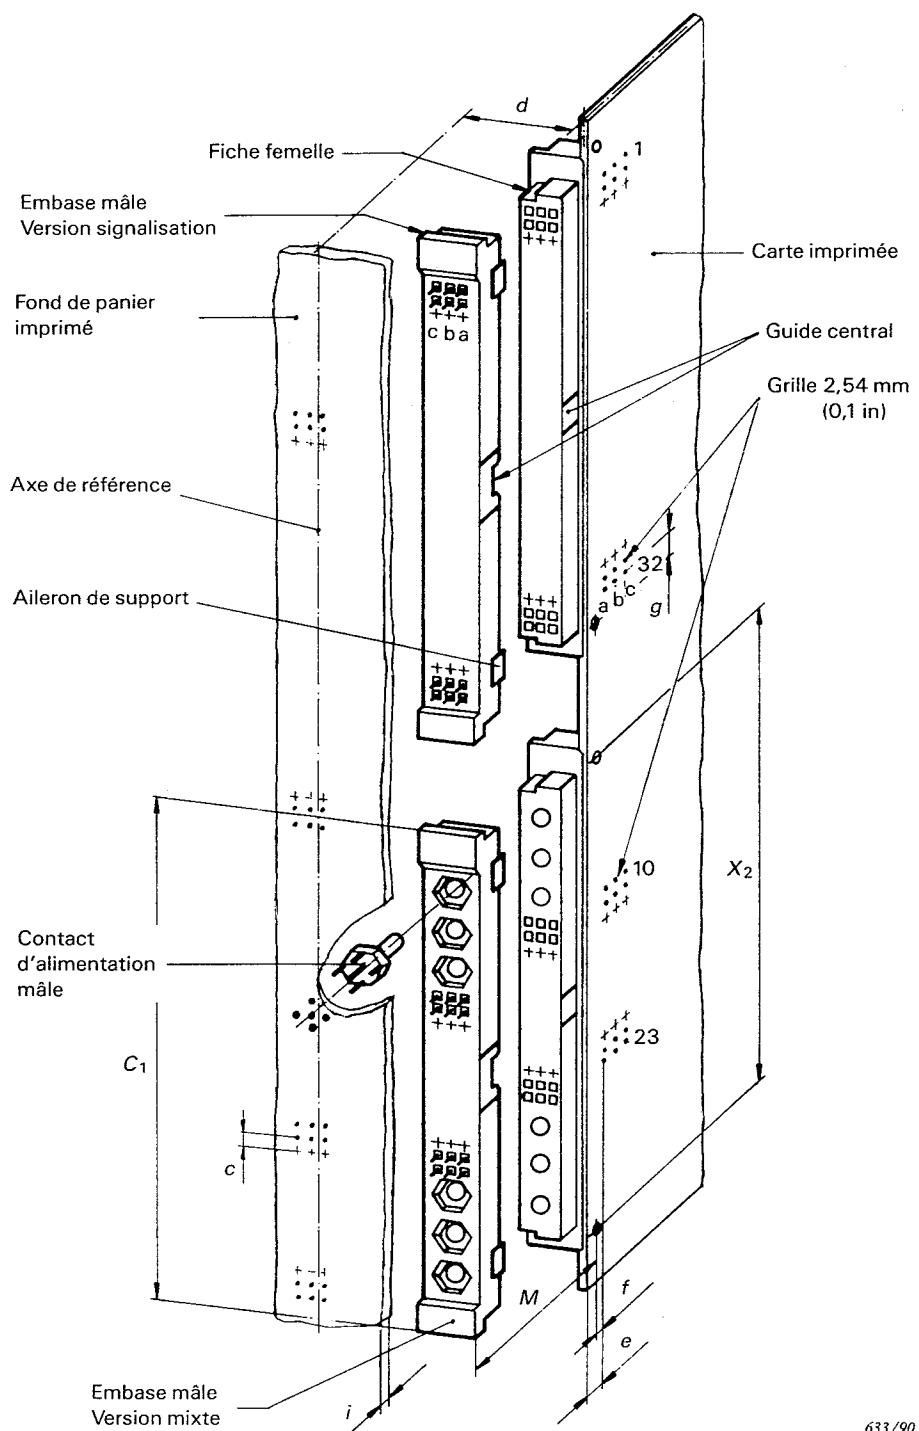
Vue isométrique et dimensions de base; système de connexion, gamme 2
